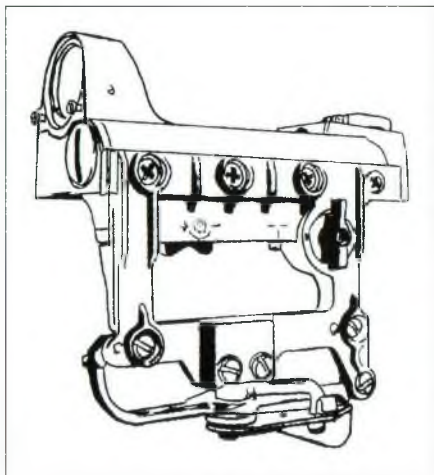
Общий вид коллиматорного прицела «Кобра» ЭКП 1С-03
